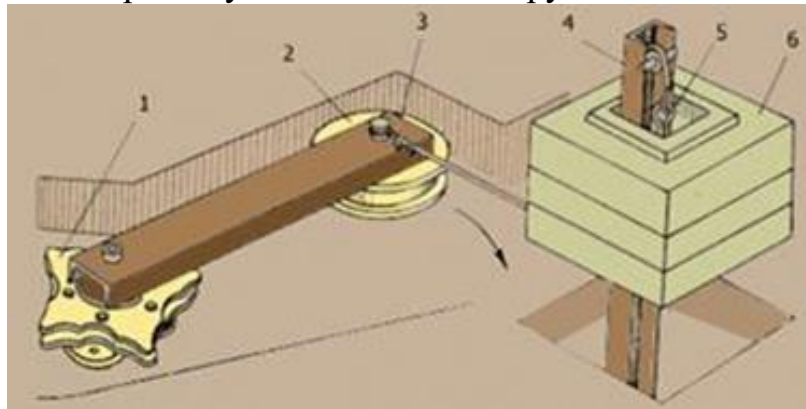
Автоматичний натяжний пристрій конвеєра КСГ-7:
